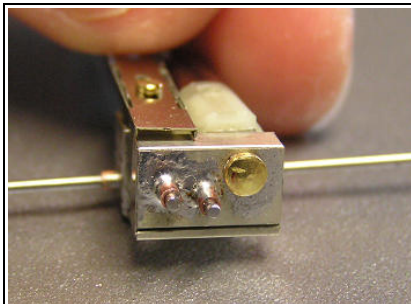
Zum Schluss wird der Deckel mit den 3 Buchsen mit etwas Sekundenkleber oder 2 kleinen Lötstellen fixiert.
